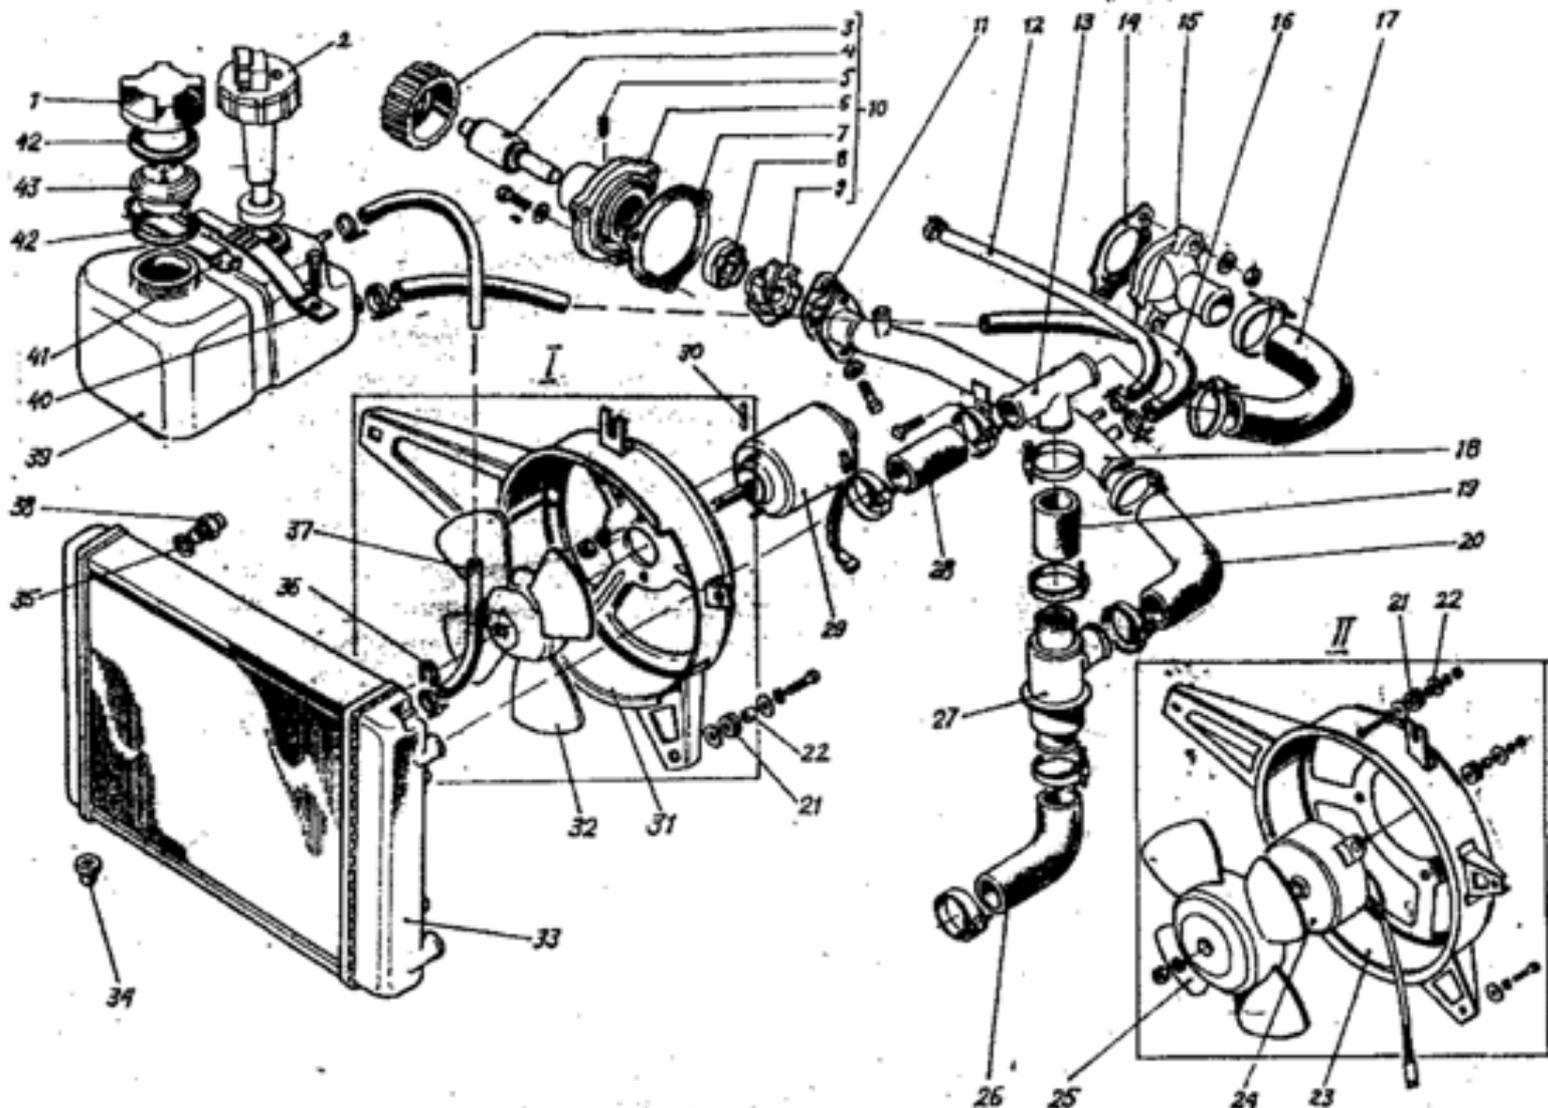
Детали системы охлаждения двигателя: 1 - корпус пробки; 2 - датчик уровня охлаждающей жидкости; 3 - шкив привода насоса; 4 - подшипник в сборе с валом; 5 - винт стопорный; 6 - корпус насоса; 7 - прокладка; 8 - манжета уплотнительная; 9 - крыльчатка; 10 - насос в сборе; 11 - прокладка; 12 - шланг к радиатору отопителя; 13 - тройник; 14 - прокладка; 15 - патрубок; 16 - шланг к расширительному бачку; 17 - шланг подводящий; 18 - труба перепускная; 19 - верхний шланг термостата; 20 - шланг от термостата к перепускной трубе; 21 - втулка; 22 - втулка дистанционная; 23 - кожух электродвигателя; 24 - электродвигатель 90 Вт; 25 - крыльчатка; 26 - шланг отводящий; 27 - термостат; 28 - шланг радиатора; 29 - электродвигатель 40 Вт; 30 - штифт; 31 - кожух вентилятора; 32 - крыльчатка; 33 - радиатор; 34 - втулка; 35 - прокладка; 36 - фиксатор; 37 - шланг пароотводящий; 38 - датчик включения электровентилятора; 39 - бачок расширительный 40 Вт; 40 - лента передняя; 41 - лента задняя; 42 - прокладка; 43 - блок клапанов; I - установка электродвигателя мощностью 40 Вт; II - установка электродвигателя мощностью 90 Вт.
